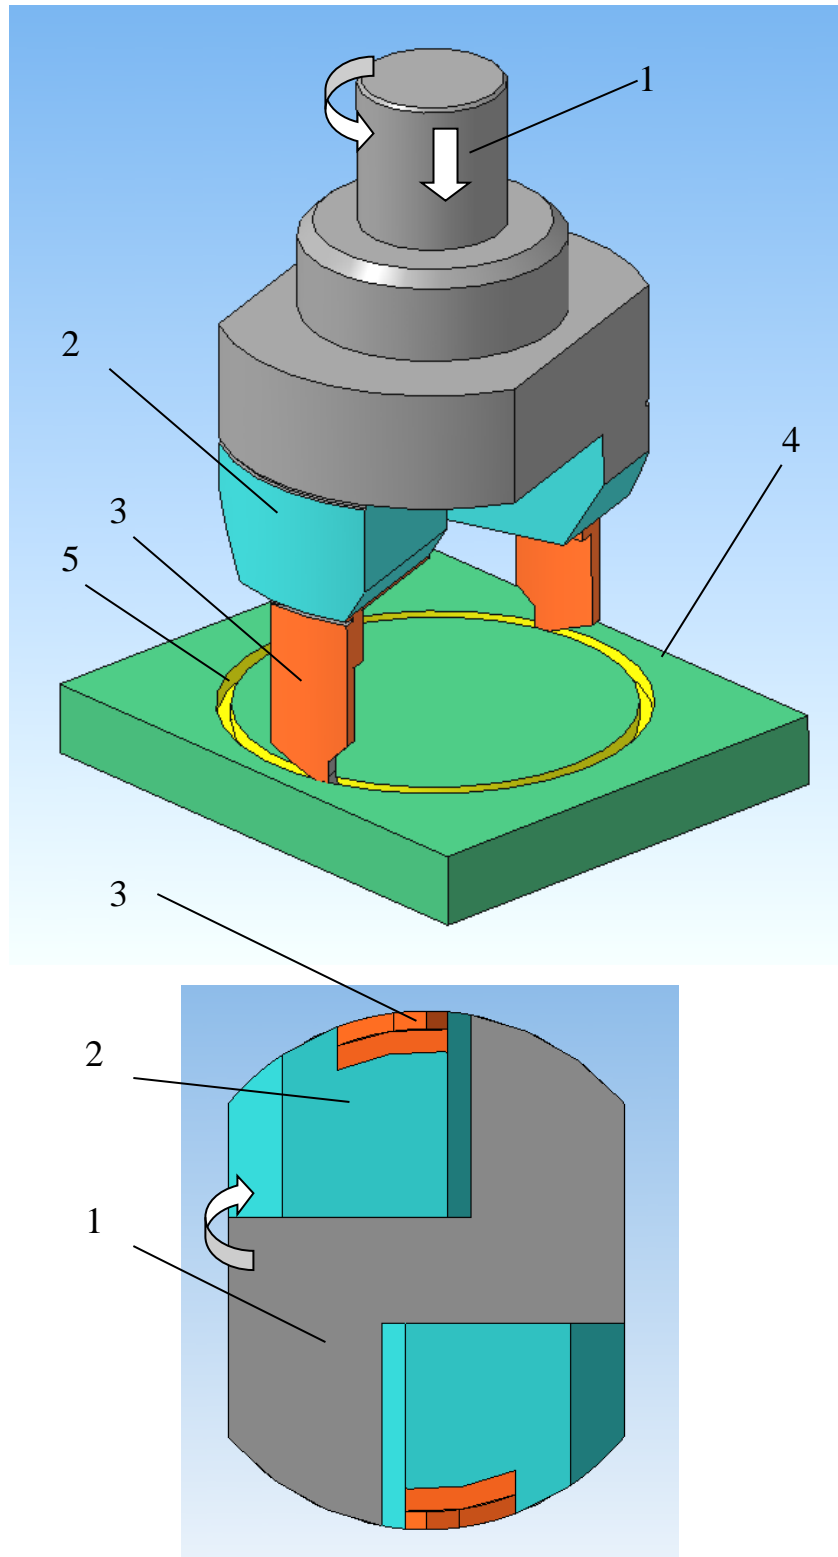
Схема процесу нарізання торцевої канавки на плоскій поверхні плити спеціальним інструментом із двома різцями: а) трьохмірне зображення; б) вигляд знизу на інструмент; 1 – оправка, 2 – картридж; 3 – різець; 4 – плита; 5 – торцева канавка
